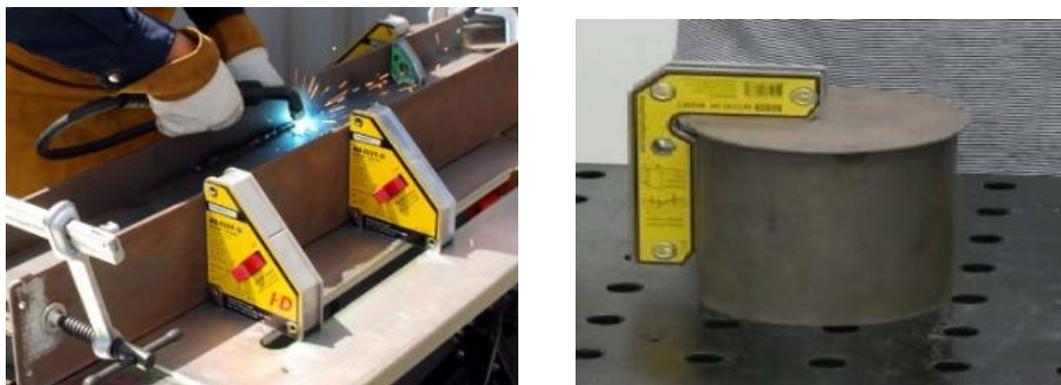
Универсальные приспособления-магниты [9]
